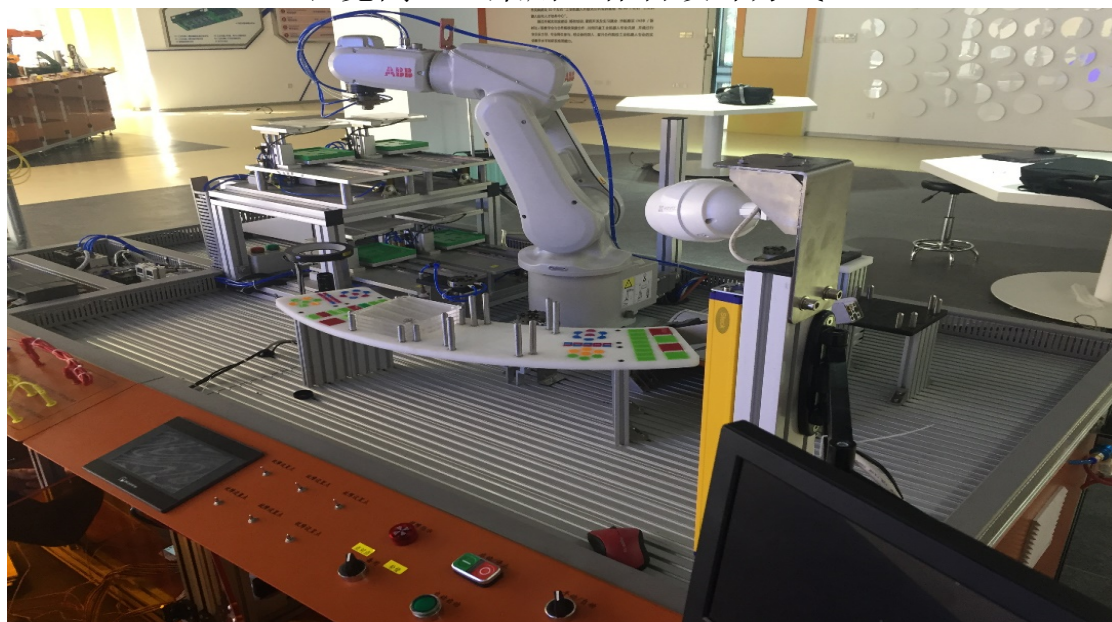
CHL-DS-01 型工业机器人 PCB 异形插件工作站
